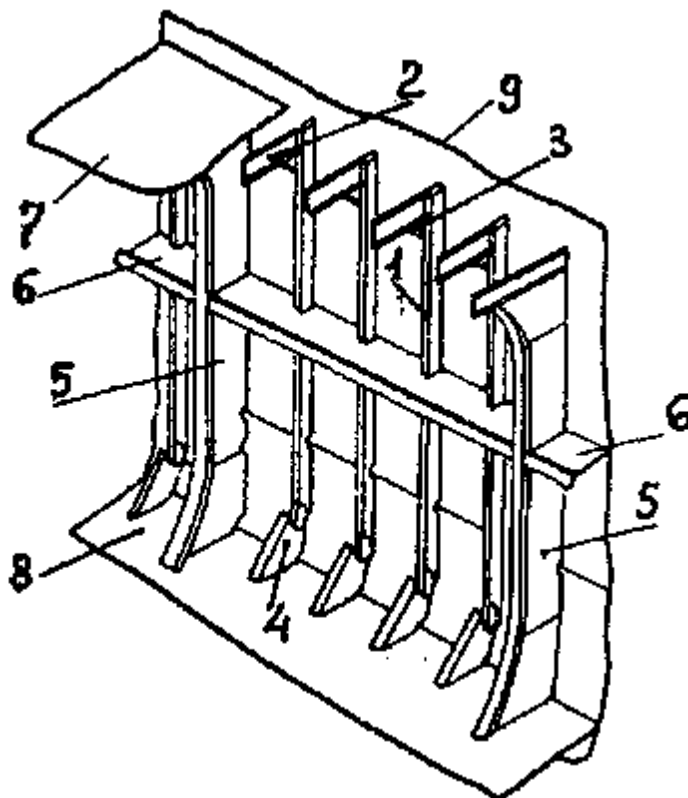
Конструкция бортового перекрытия при поперечной системе набора:
